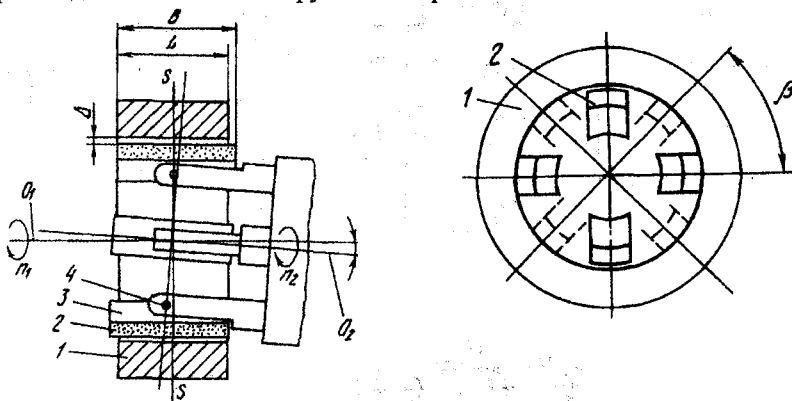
Способ обработки дорожек качения роликоподшипников
